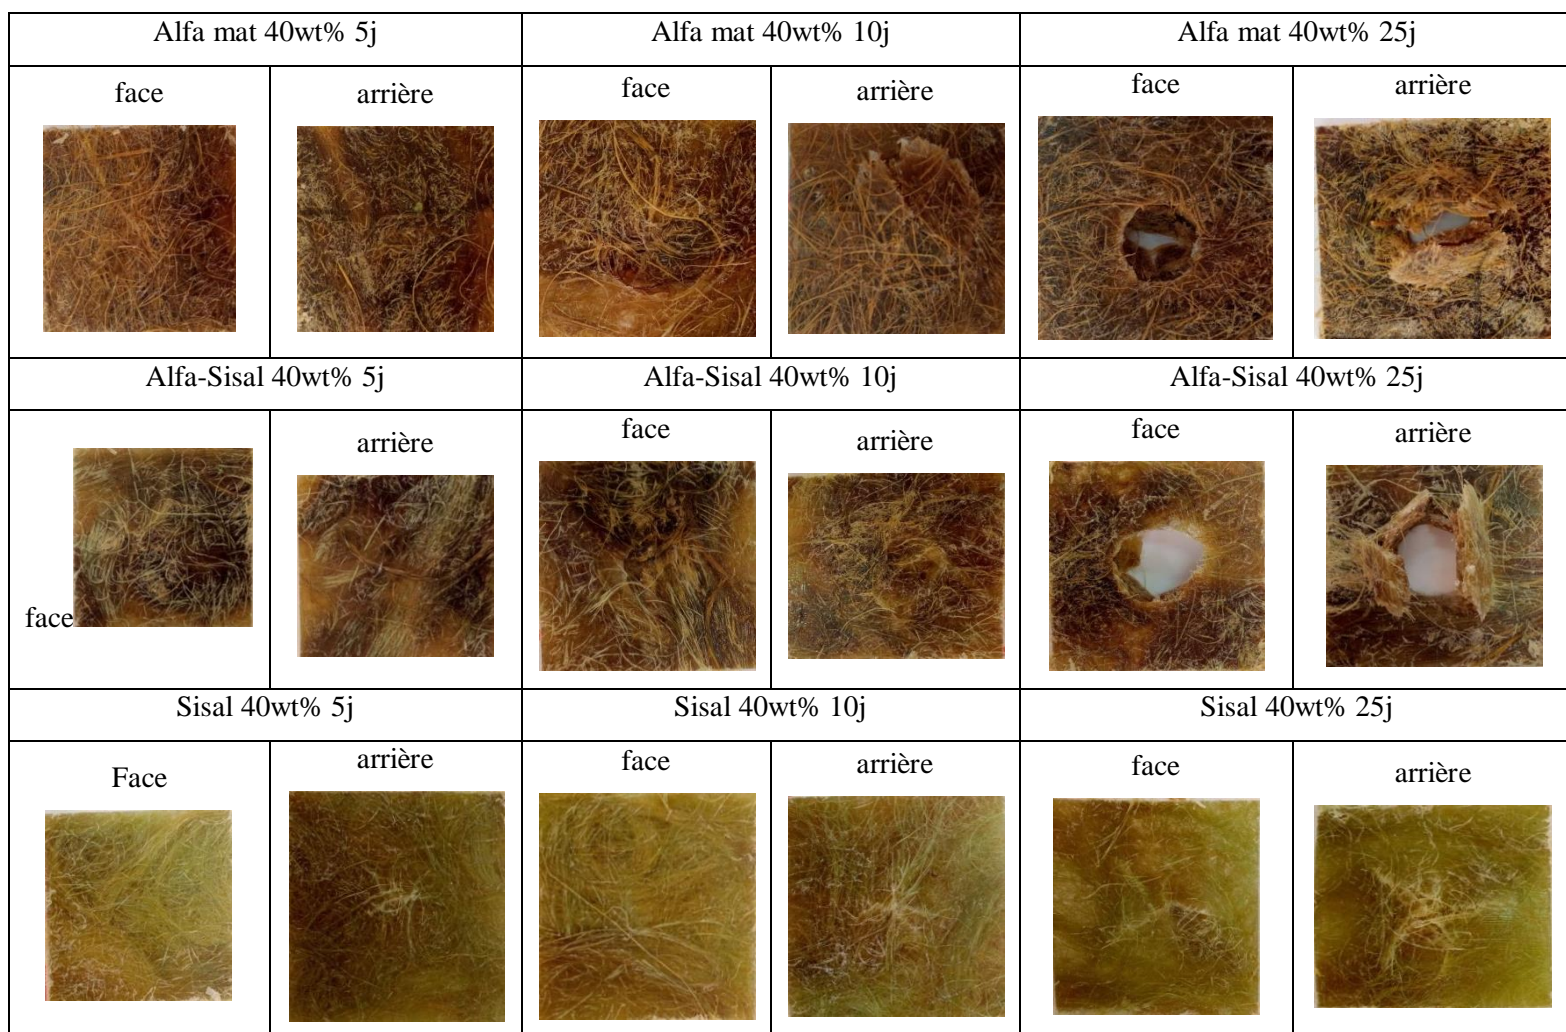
Vues avant et arrière des éprouvettes après essai d'impact.
